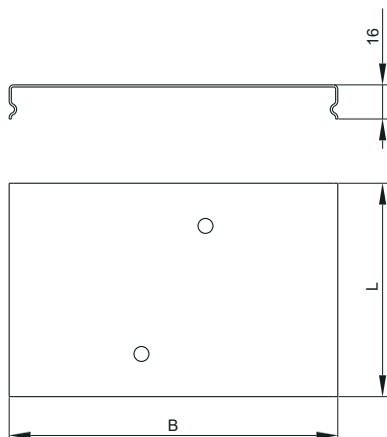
накладка для крышки лотка / Figure B.1 – Tray cover plate
